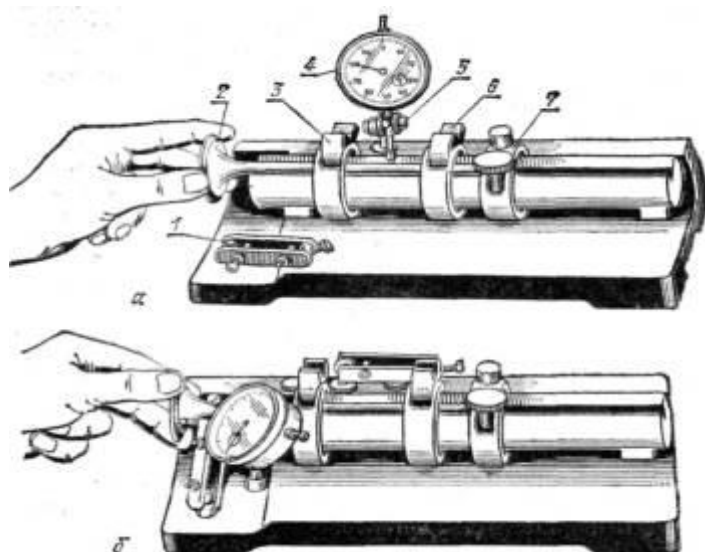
Проверка клапана на индикаторном приспособлении:
